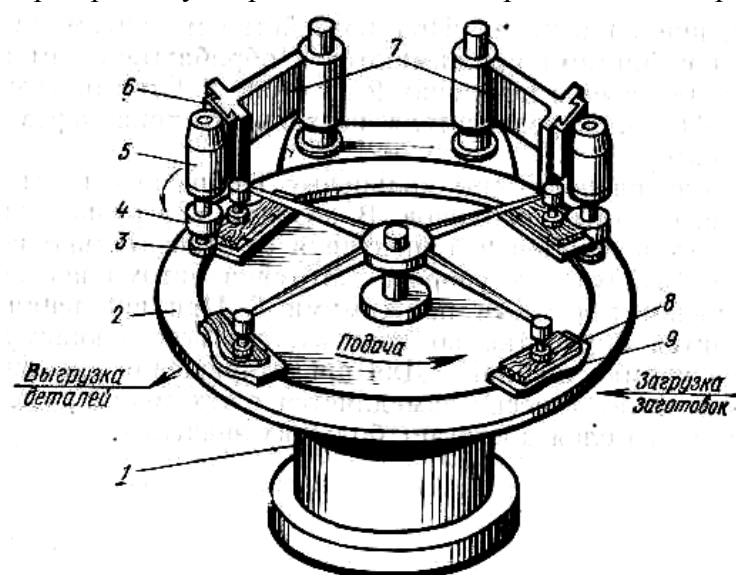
Двухшпиндельный фрезерный карусельный станок Ф2К-2:
